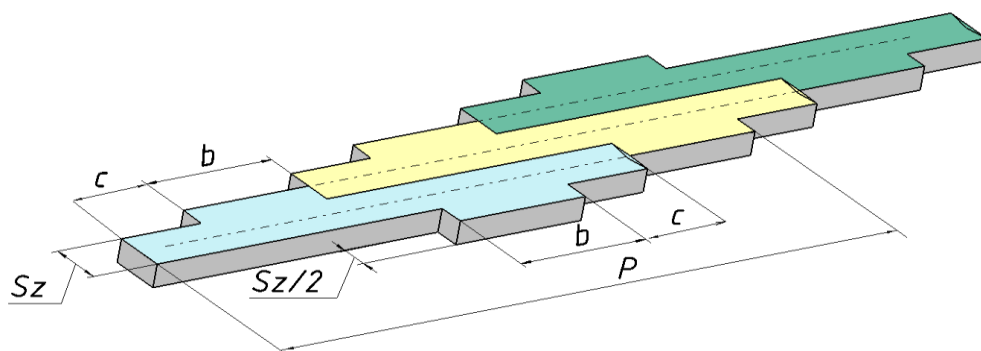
Ячейки поверхности, образованной фрезой с геометрией типа «Стружколом»
